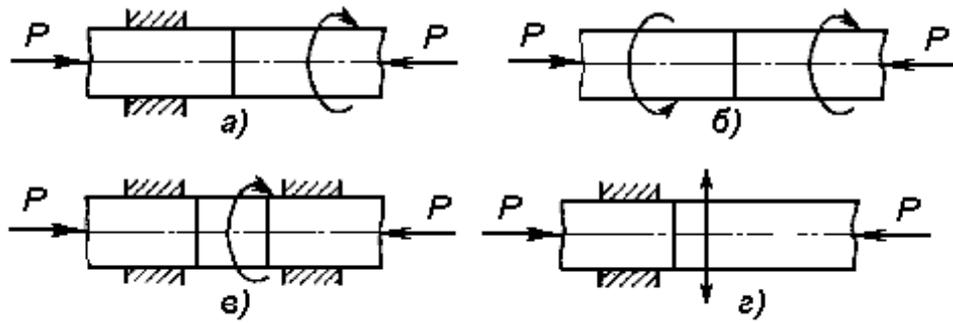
Принципиальные схемы сварки трением
